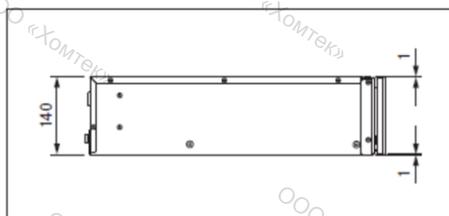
Размеры прибора, модель MSS140, вид сбоку
